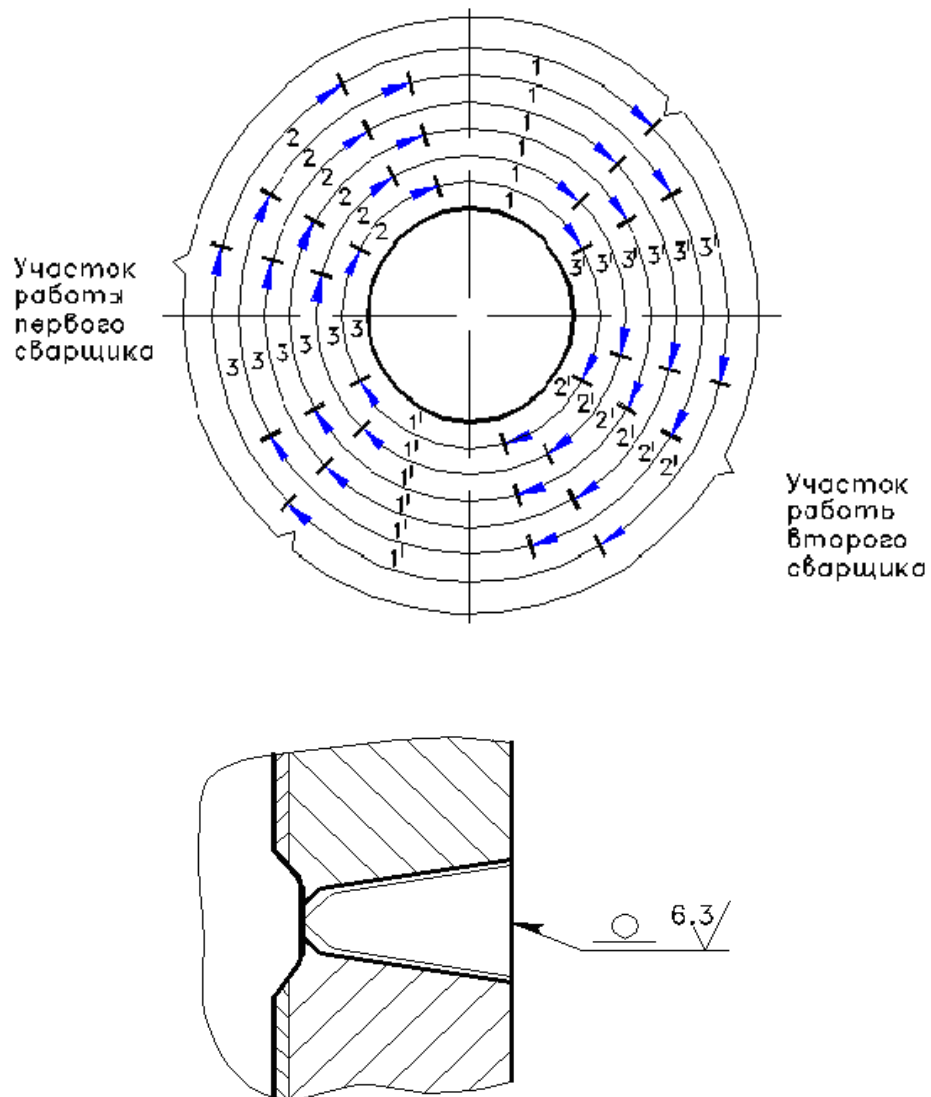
Порядок сварки и выполненное сварное соединение трубы узла трубного и коллектора парогенератора (до восстановления плакирующего слоя)
